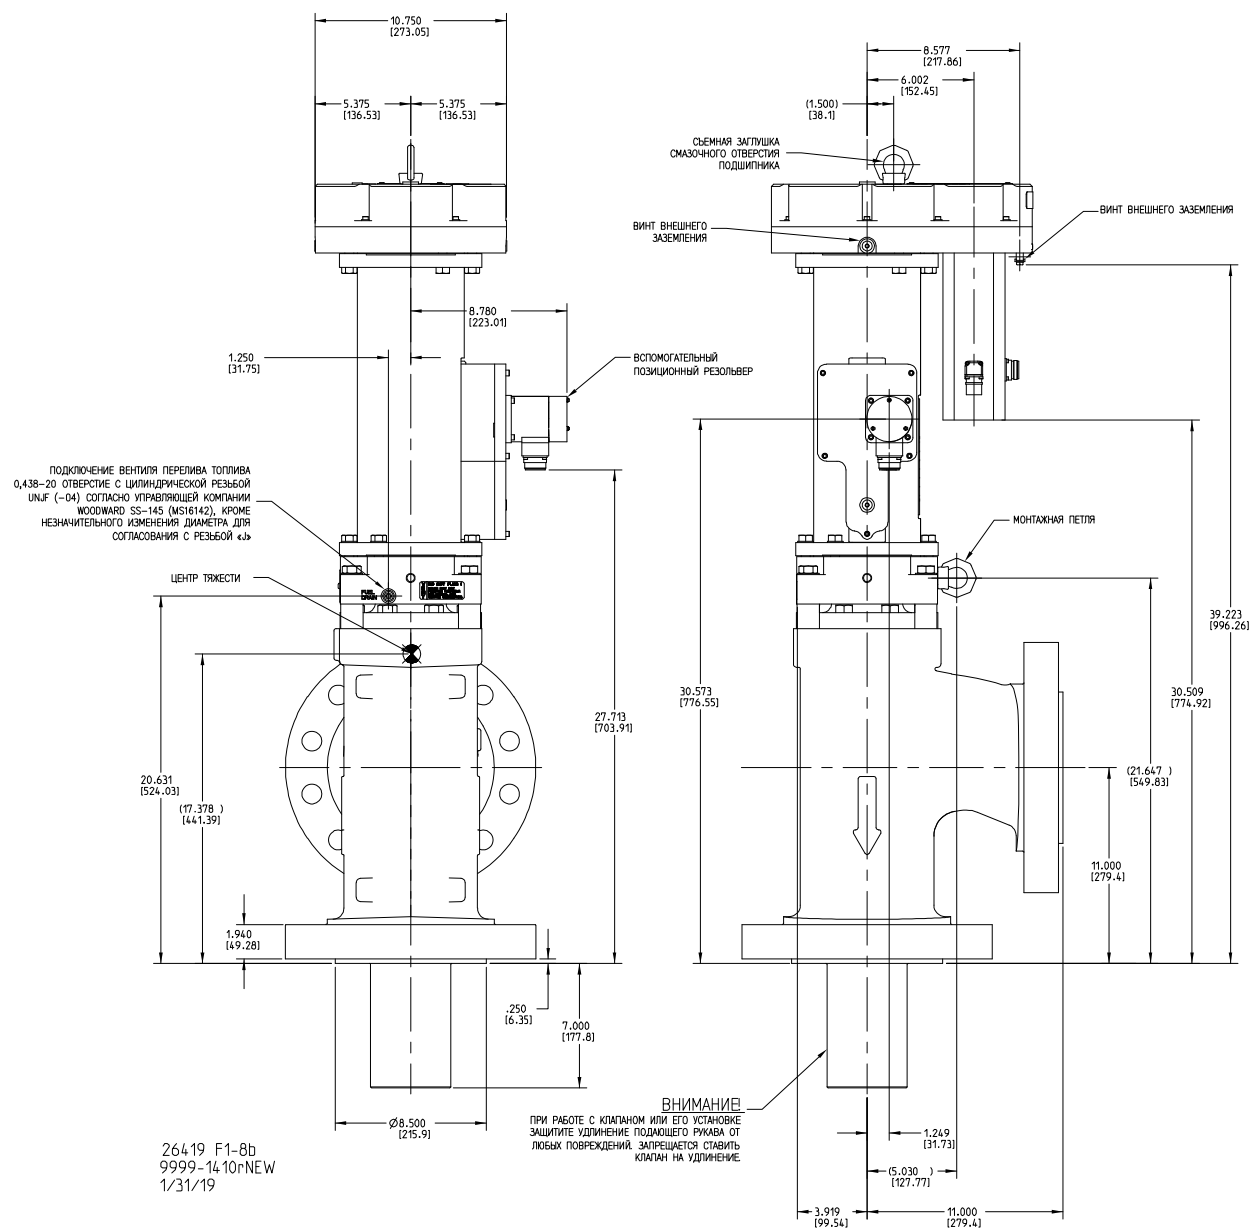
Габаритный чертеж (6-дюймовый клапан LESV класса 600)
